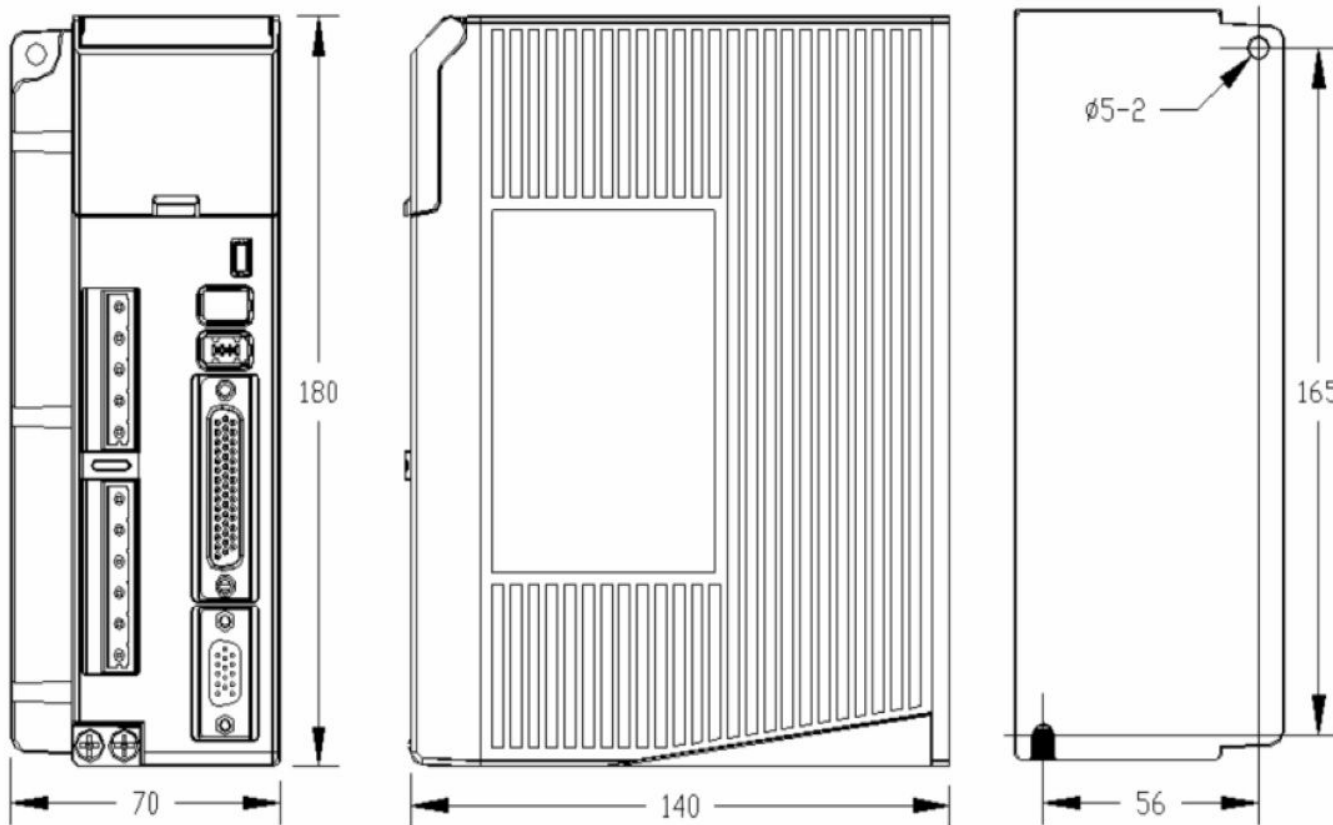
Габаритные размеры серводрайвера ES-DH2306
